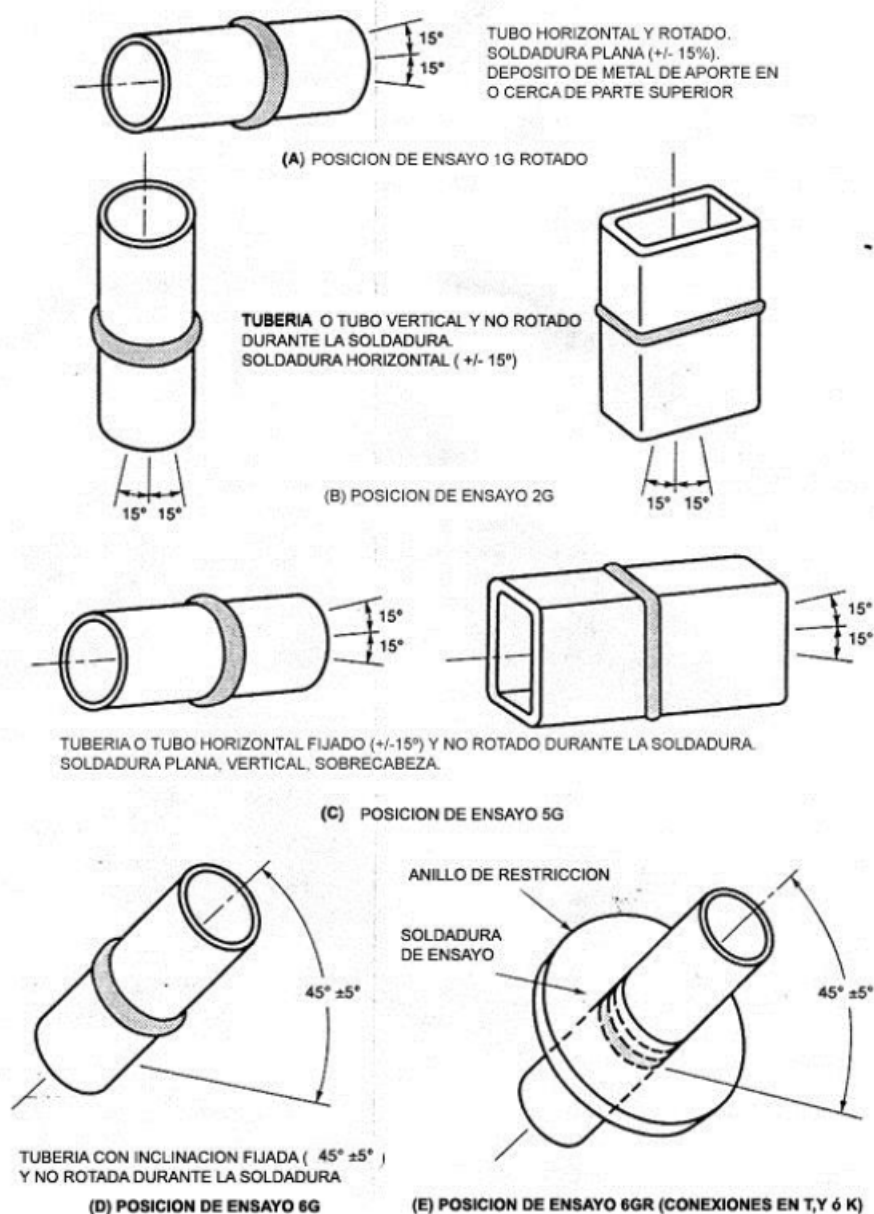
Posiciones de Tubo o Entubado de Ensayo para Soldaduras de Ranuras (ver 4.2.4)
